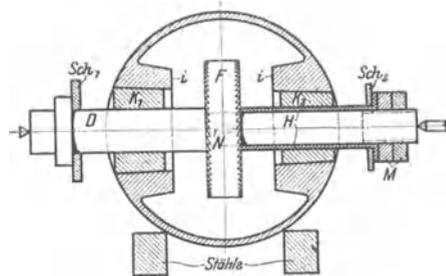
Abfräsen der Augen für die Kolbenbolzen.
